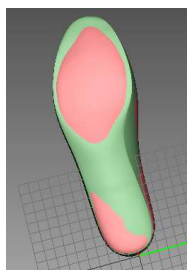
Vergleich plan zu ballig: Plantare Ansicht des Damenhalbschuhs;
